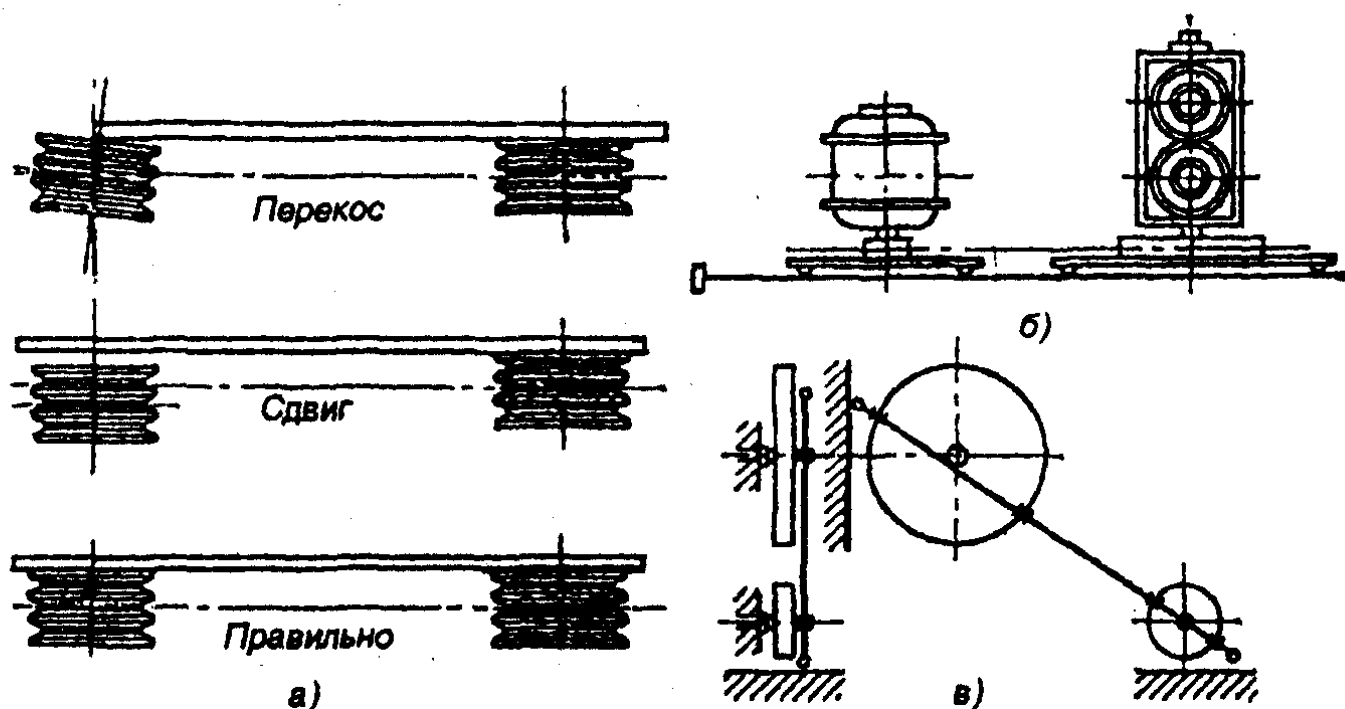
Способы выверки установки электродвигателя при ременной и клиноременной передачах и одинаковой ширине шкивов с помощью линейки (а), скоб и струны (б), шнура(в)
